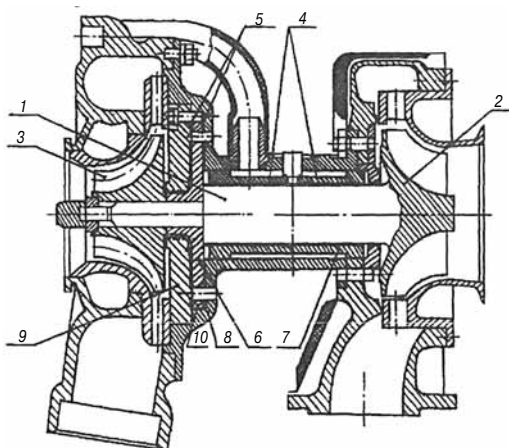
Турбокомпрессор с лепестковыми газодинамическими подшипниками:
